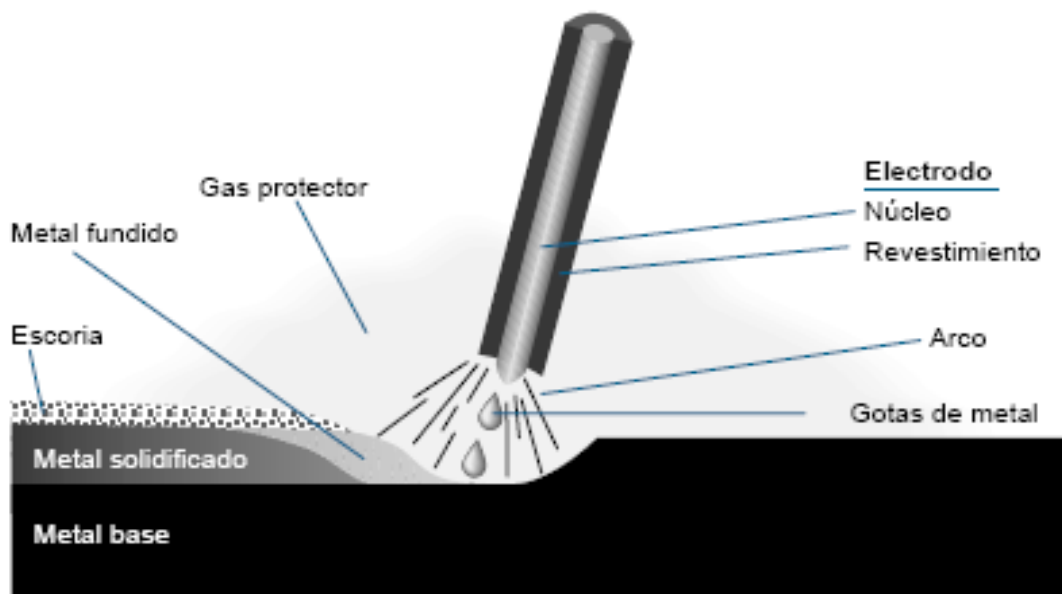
Proceso de soldadura por arco metálico protegido.
